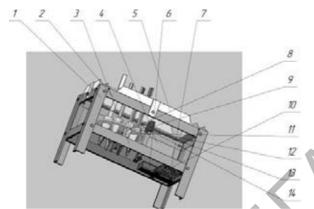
Конструкция МОПГ (днище и крышка показаны прозрачными) 1,3,2,4 — конструктив несущей рамы, 5 — посадочное место, 6 — аккумуляторная батарея, 7 — площадка для управляющей электроники, 8 — сервопривод поворотного стола, 9 — сервопривод подъёмного механизма, 10 — фиксатор аккумуляторной батареи, 11 — вал сервопривода, 12 — поворотный стол, 13 — сервопривод подъёмного механизма, 14 — плечо подачи лопатки.
